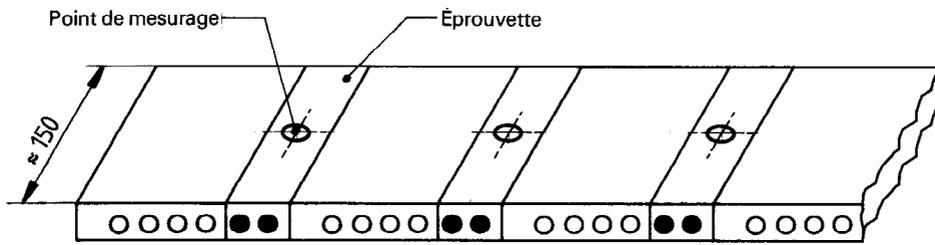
Éprouvettes prélevées aux points de mesure dans toute la largeur de la courroie
